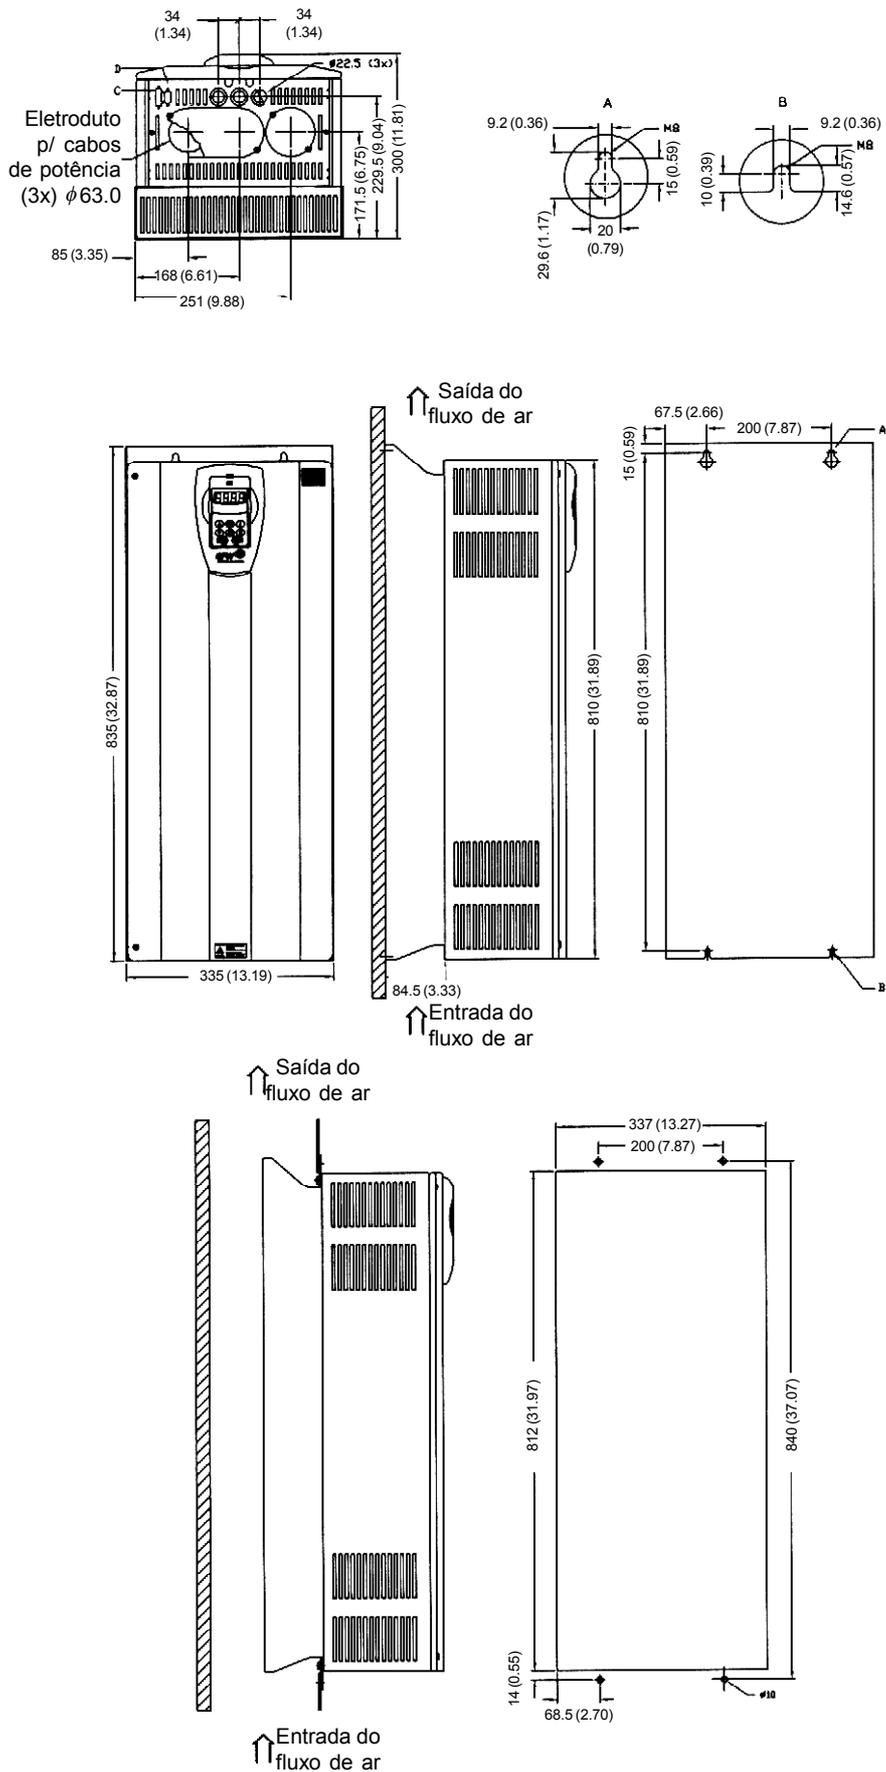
Mecânica 7 - Dimensões em mm (polegadas)
